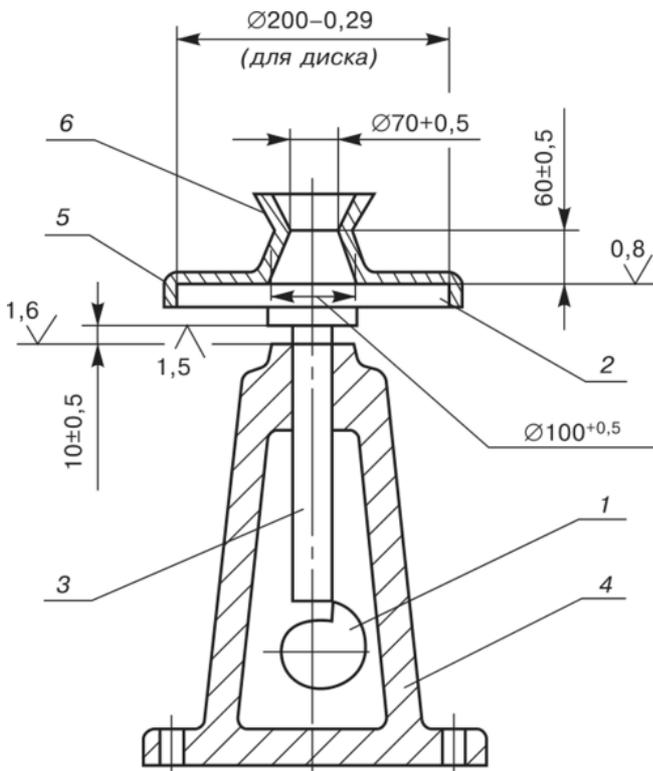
Встряхивающий столик: 1 — кулачок; 2 — диск; 3 — шток; 4 — станина; 5 — форма-конус с центрирующим устройством; 6 — насадка
